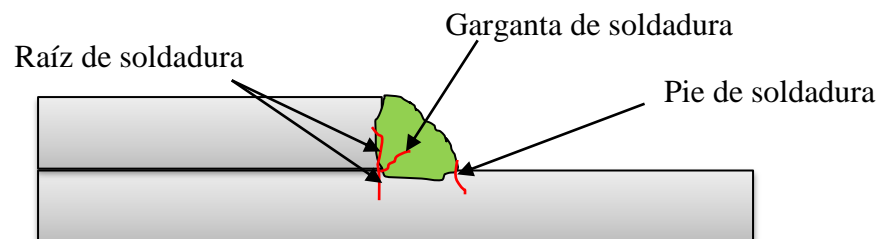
Apoyo tipo placa sobrepuesta
